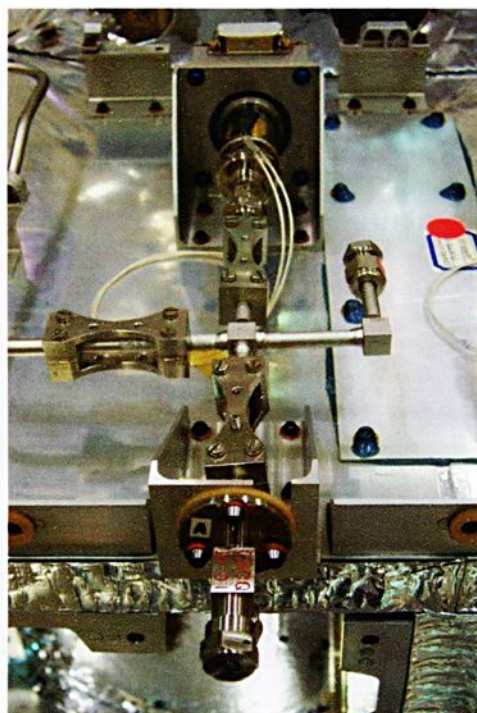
Utilização de braçadeiras para o posicionamento correto
